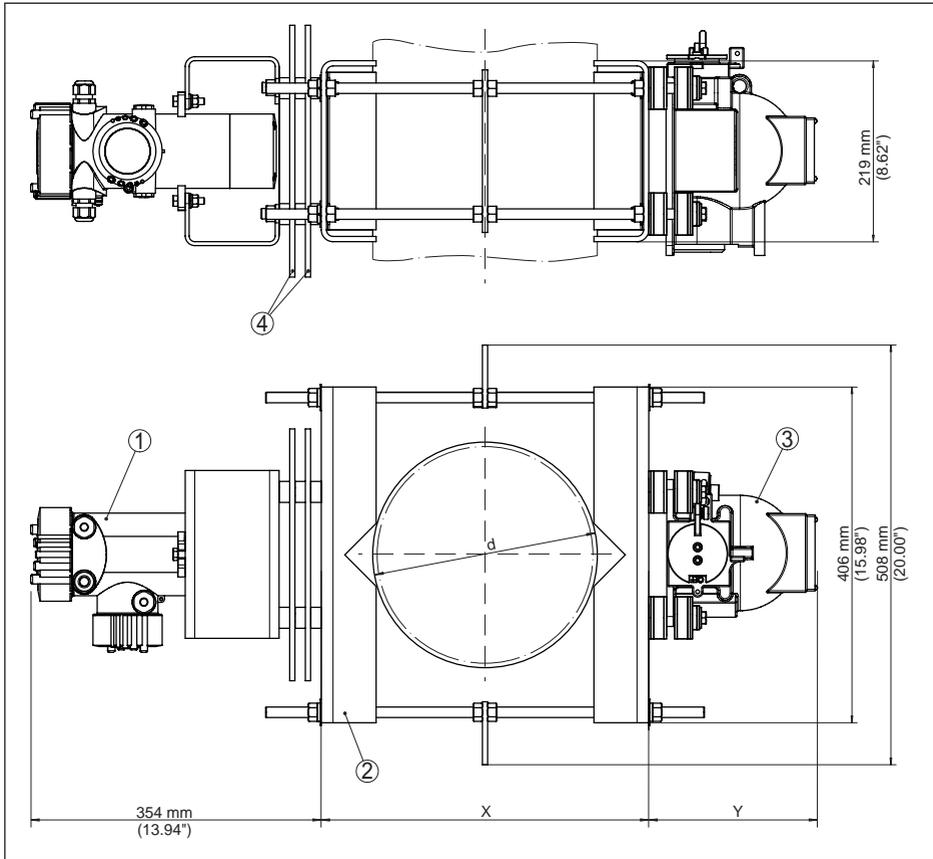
Dispositivo de sujeción con contenedor de protección de fuente radiactiva SHLD1, sensor montado horizontalmente y kit de protección térmica
